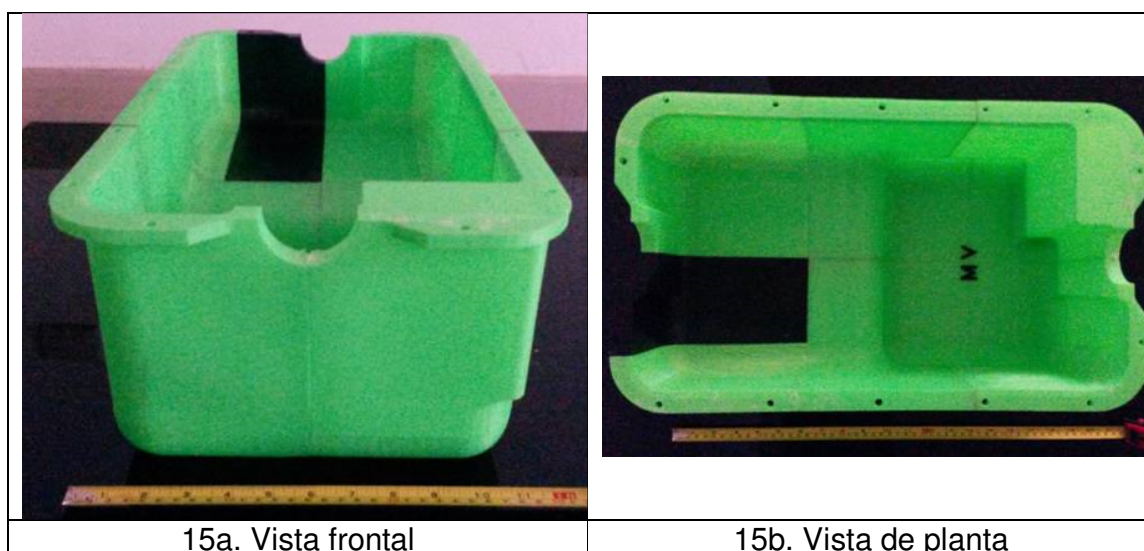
Cáster ensamblado (vistas frontal y de planta)
